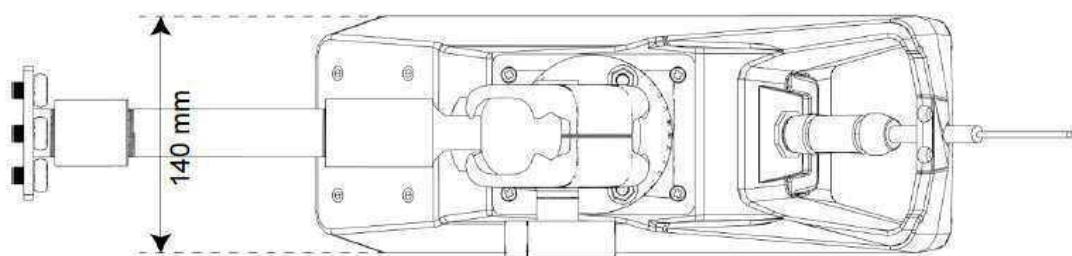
Vista en planta de las dimensiones del sensor RAVEN EYE según se ha instalado
